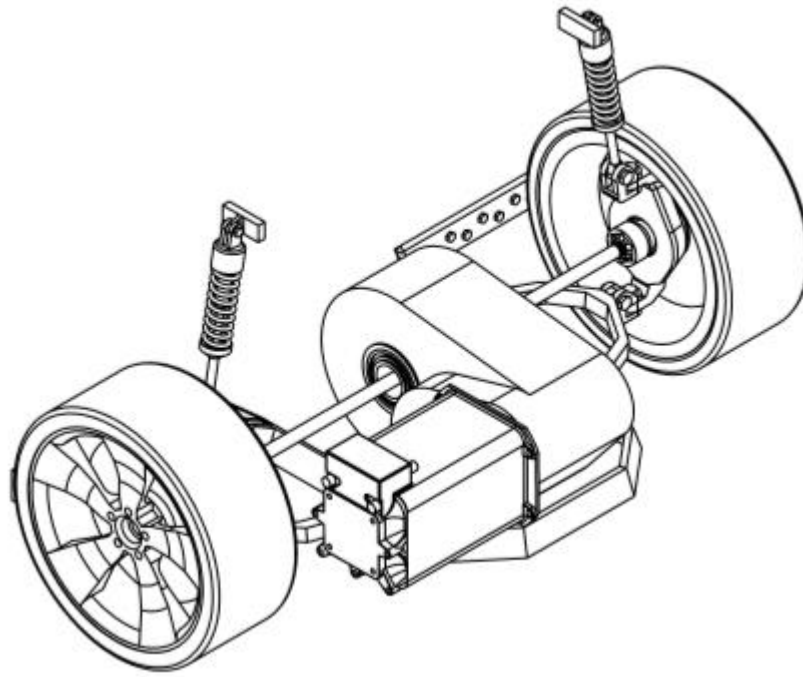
Загальний вигляд заднього приводу(Вид ізометричний).
